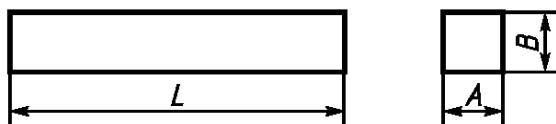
Размеры образца для испытания на ударный изгиб
